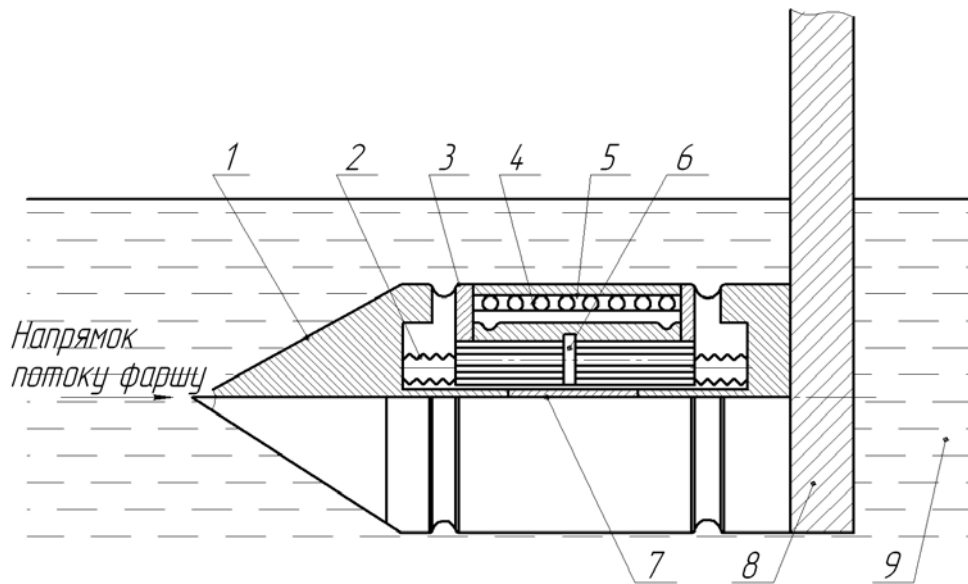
Конструктивна схема віскозиметра для вимірювання СМХ фаршу в потоці: 1 - корпус; 2-сильфони; 3-кільцеві мембрани; 4-давач з рифленою поверхнею; 5 - нагрівальний елемент; 6 - дифтрансформаторний перетворювач; 7 - сердечник перетворювача; 8 - кронштейн; 9 - фарш
